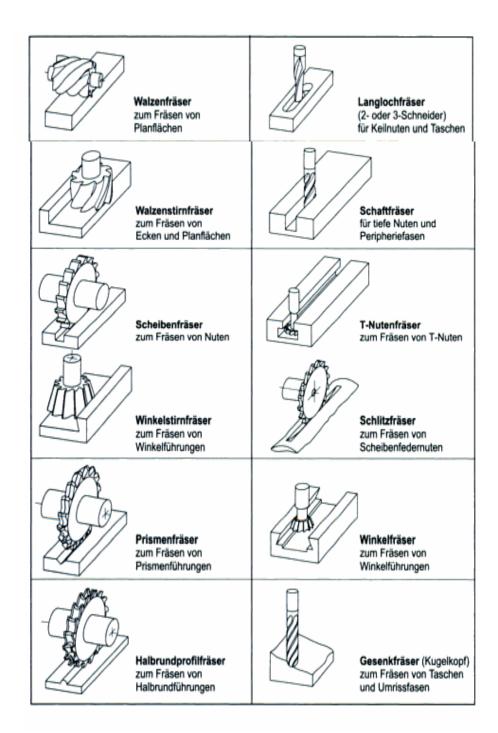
Fräswerkzeuge und einige typische Anwendungen / Freze şi domenii de utilizare [WES 18]
